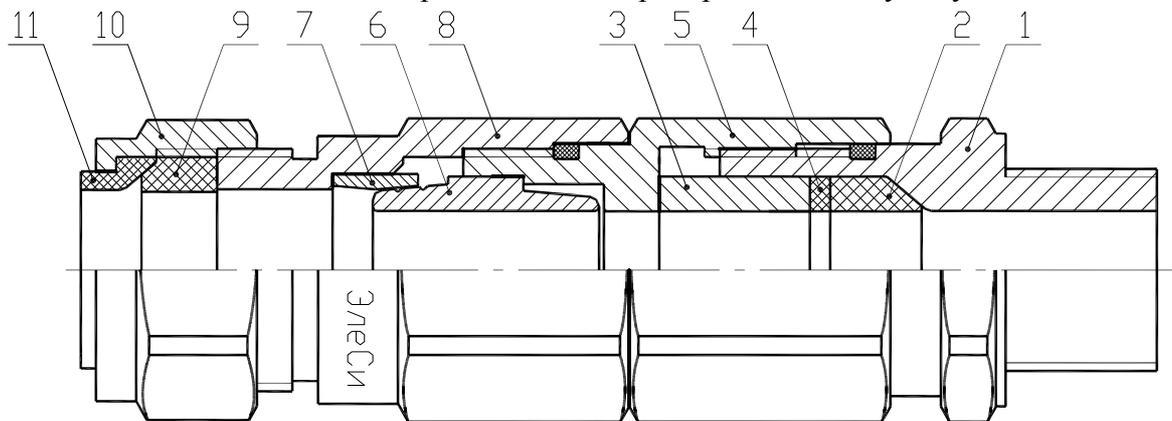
Конструкция кабельного ввода ExCG А для монтажа бронированного кабеля
